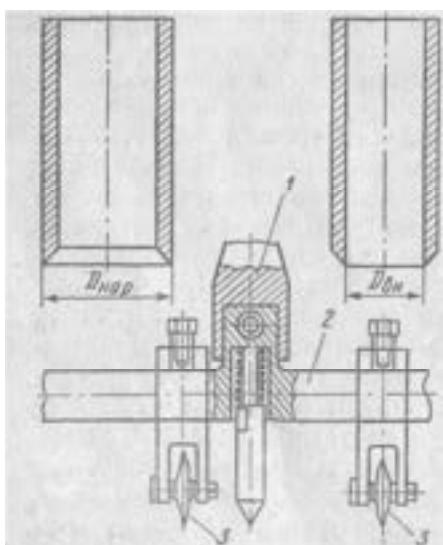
Приспособления для вырубки и вырезки прокладок:
